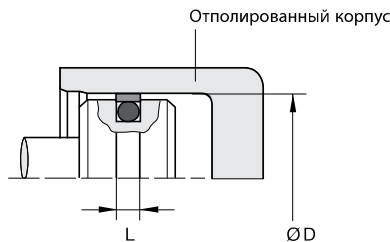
Slipper Seal®поршневого типа, установка, шаг 4. Изменение размера уплотнения Slipper Seal®поршневого типа.
